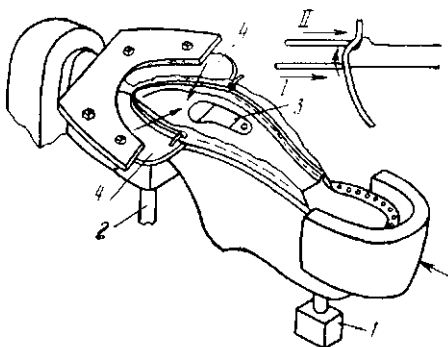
Схема затяжки носочной части заготовки верха обуви пластинами
